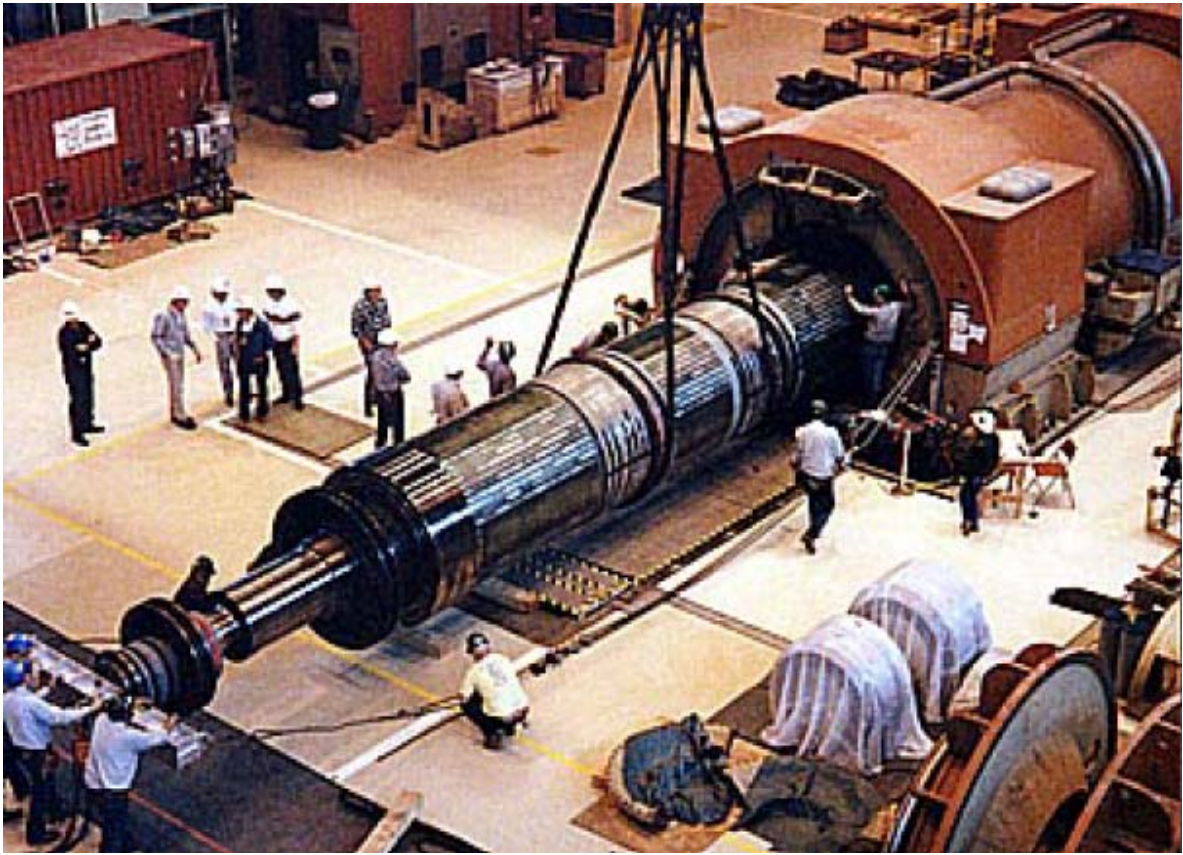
f: Montagem de rotor de turbogerador (adaptado de P. C. Sen, Principles of electric machines and power electronics)
